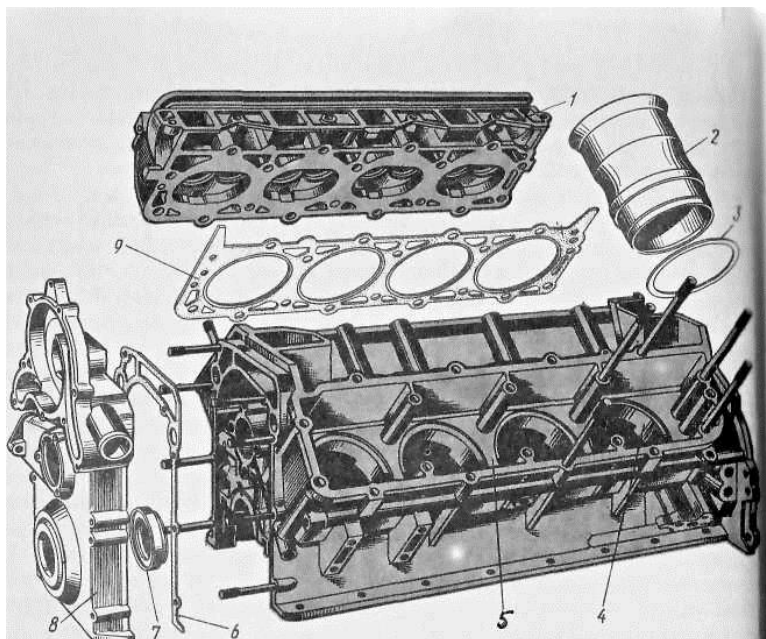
Головка и блок цилиндров V-образного восьмицилиндрового двигателя ЗМЗ-53: 1 - головка правого ряда цилиндров, 2 - гильза цилиндра, 3 - прокладка гильзы, 4 - направляющий поясok для гильзы, 5 - блок цилиндров, 6 - прокладка крышки распределительных шестерен, 7 - сальник переднего конца коленчатого вала, 8 - крышка распределительных шестерен, 9 - прокладка головки цилиндров
